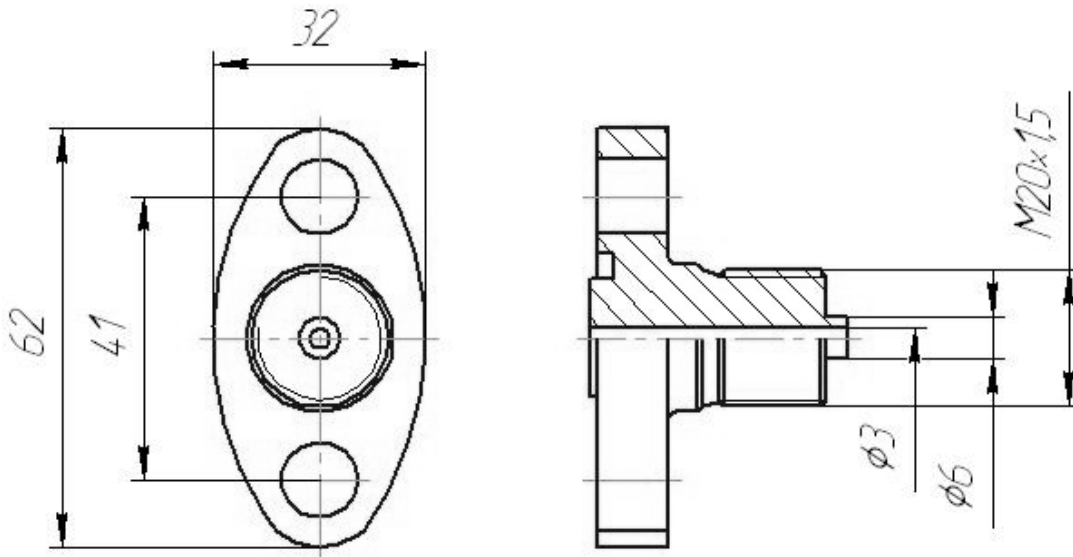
Фланец с резьбой M20x1,5 под плоский ниппель – M2H
